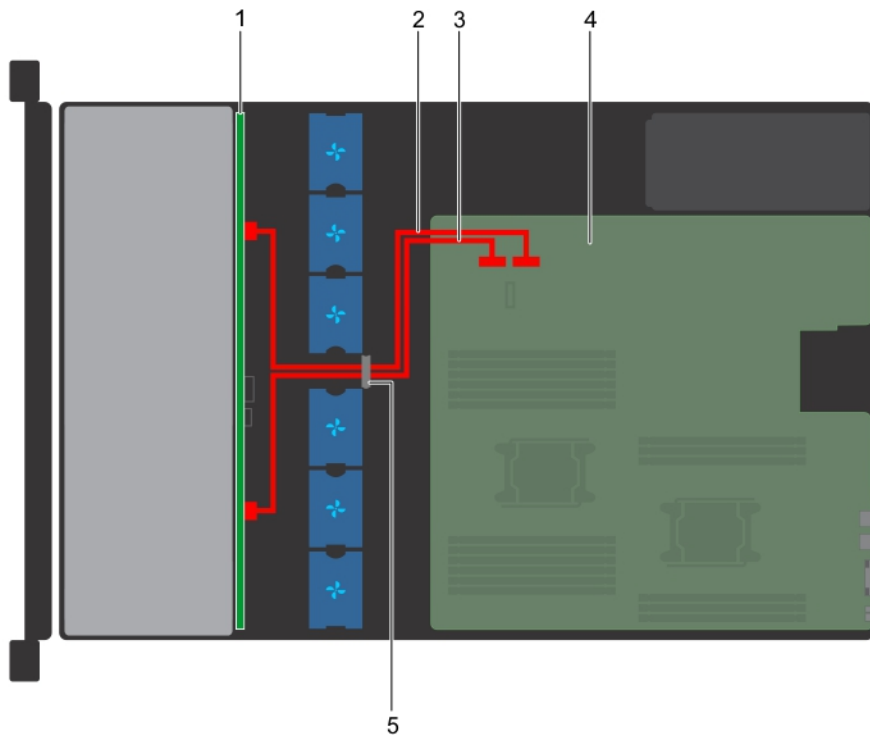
Acheminement des câbles : fond de panier à 8 disques de 3,5 pouces
